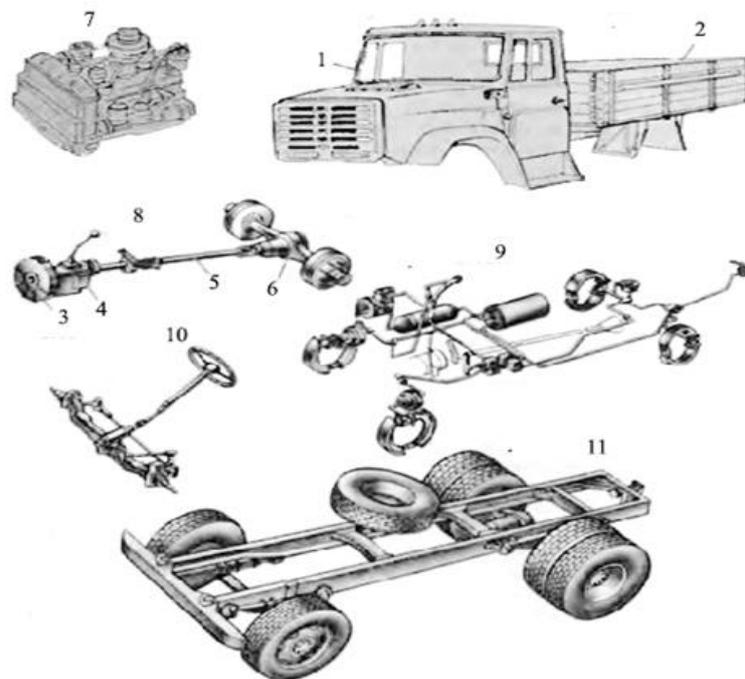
Общее устройство грузового автомобиля: 1 — кабина; 2 — грузовая платформа; 3 — сцепление; 4 — коробка передач; 5 — карданная передача; 6 — ведущий мост; 7 — двигатель; 8, 9 — трансмиссия; 10 — рулевое управление; 11 — ходовая часть.
